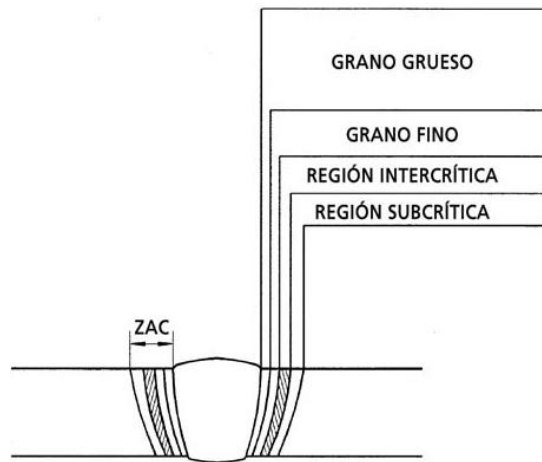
Imagen que ilustra la zona afectada por el calor en una soldadura
